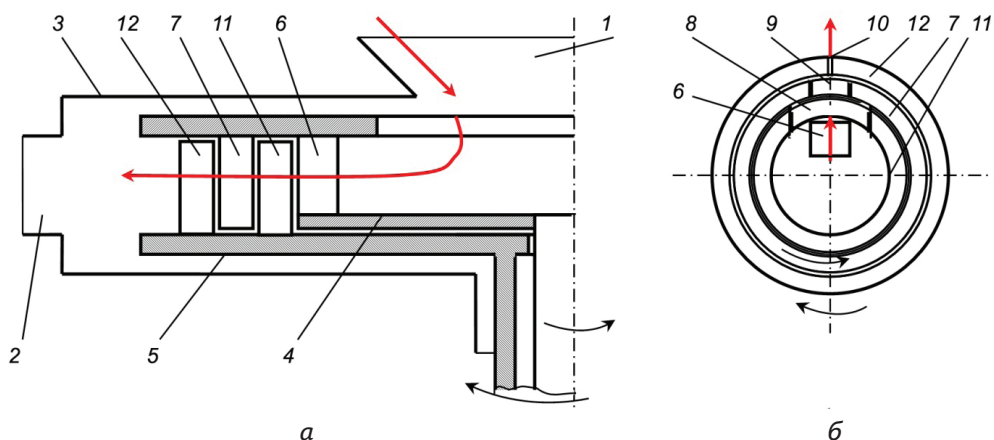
Рабочий орган измельчителя роторного встречного удара: а – вид с боку; б – вид со стороны разгрузочного окна
